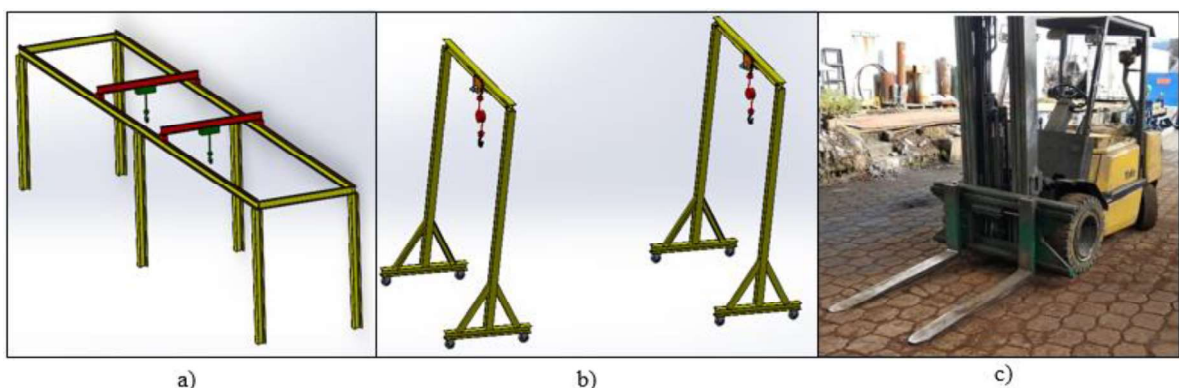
a) pórtico fijo, b) pórtico móvil, c) monta cargas.
